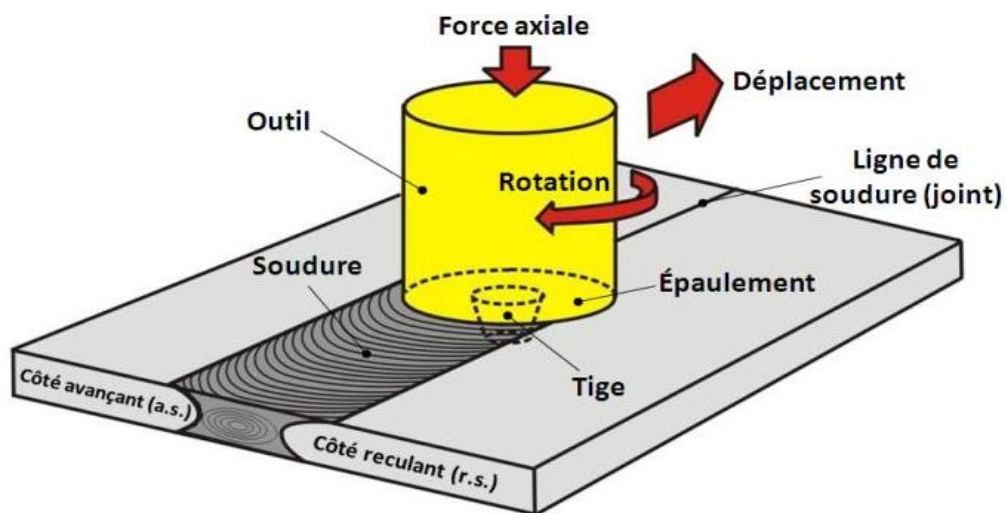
Soudage par friction malaxage. [5]
